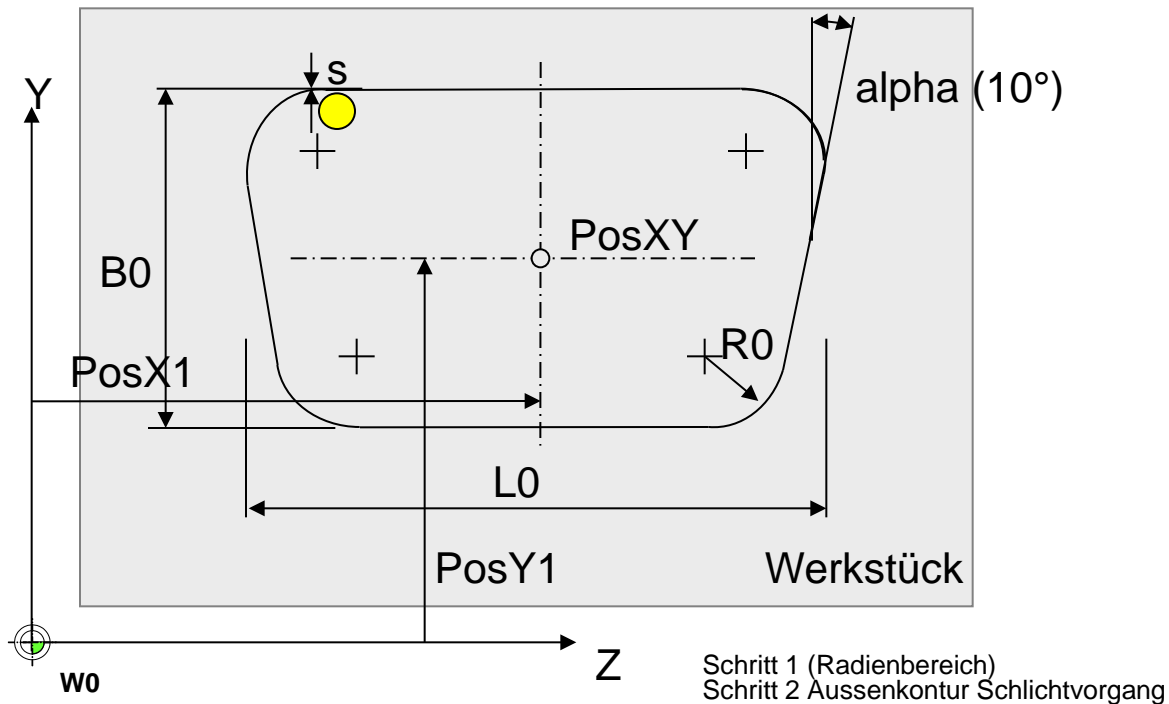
Parameter für die Definition einer rechteckigen Frästasche
